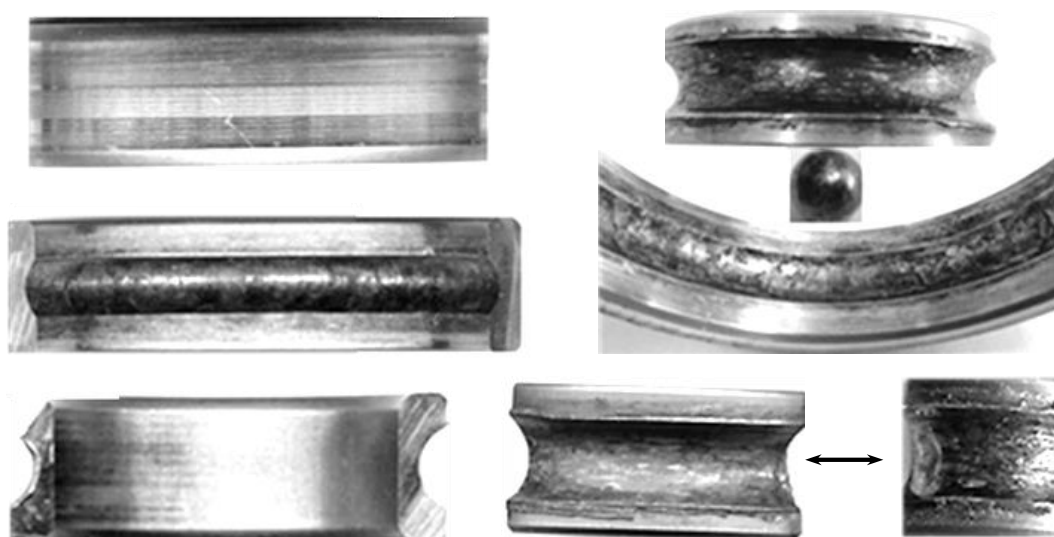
Внешний вид фрагментов, нерабочих поверхностей и дорожек качения вышедшего из строя шарикоподшипника
